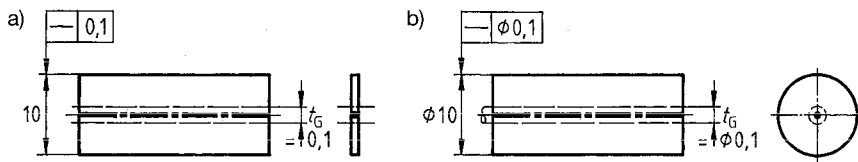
Gestalt von Toleranzzonen, hier zur Tolerierung einer Mittellinie bzw. Achse. a) ebenflächig begrenzt, b) kreiszylindrisch (röhrenförmig)
